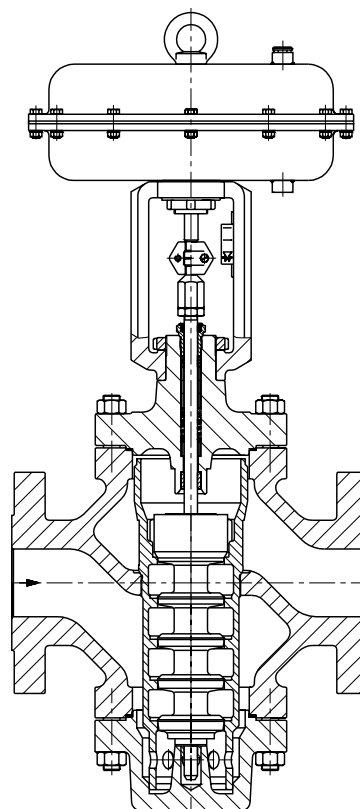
· Stellventil Typ 255-1 mit fünfstufigem Axialkegel
